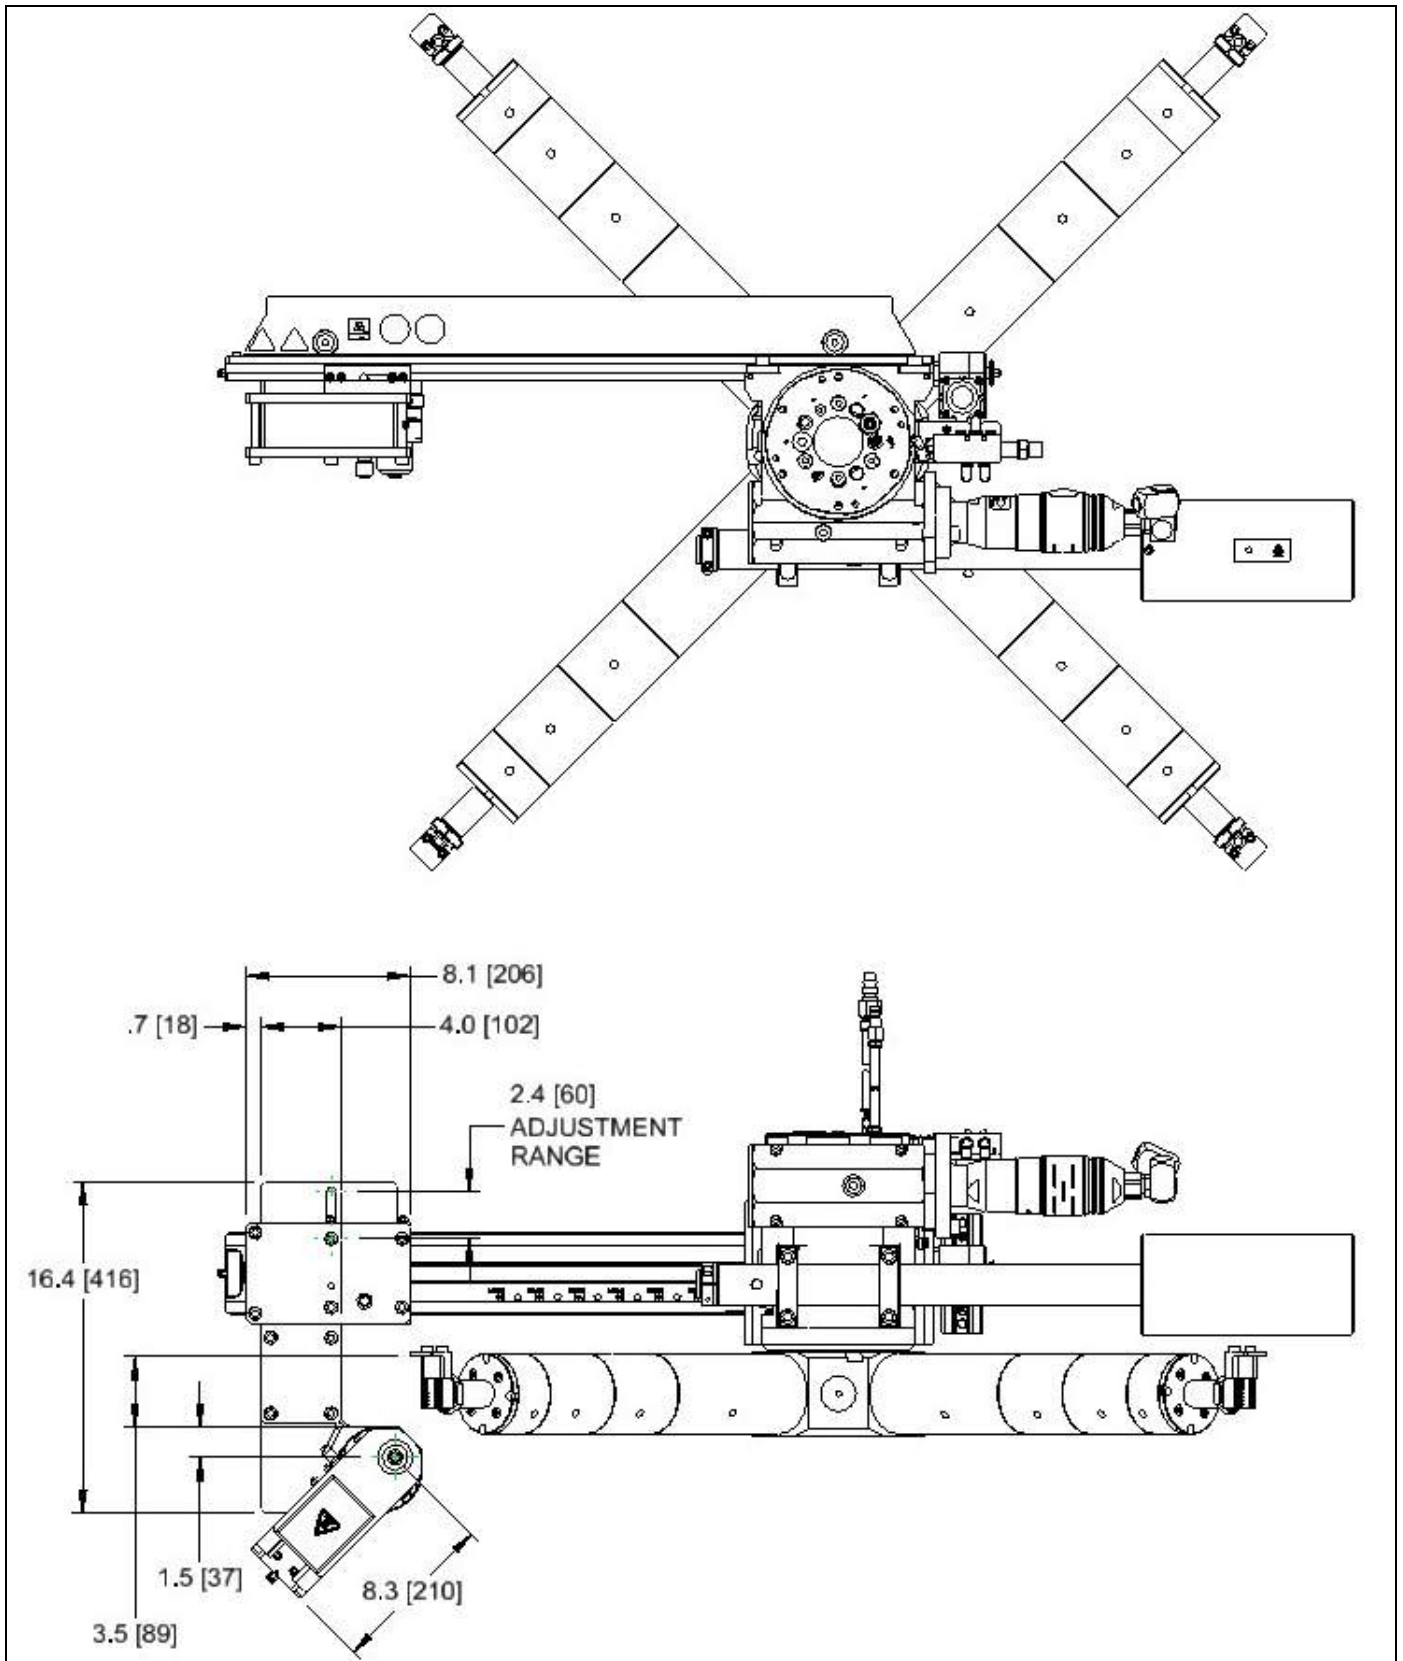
FF6300 DIMENSIONS DE LA FIXATION EN FACE ARRIÈRE
